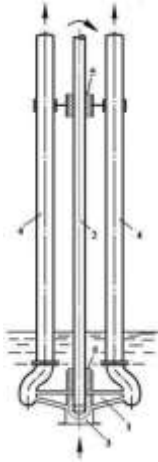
Схема заглибного насоса: 1 – робоче колесо; 2 – вал; 3 – всмоктувальний патрубок; 4 – напірні труби; 5 – підшипник
